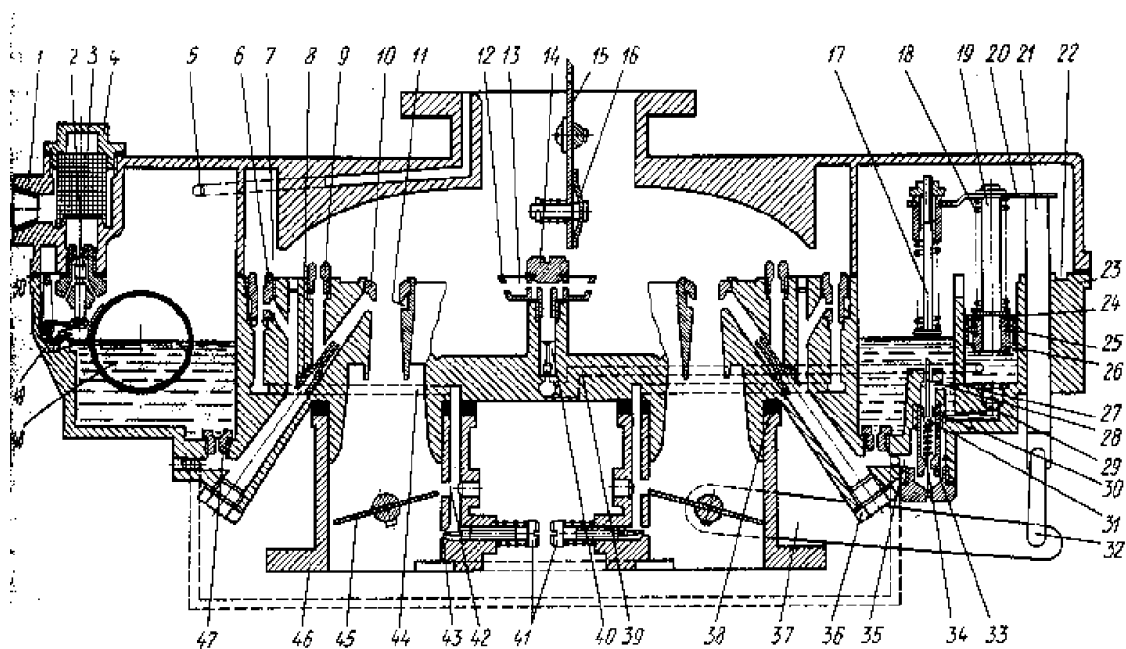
Схема карбюратора К-88АМ. 1-корпус воздушной горловины; 2-игольчатый клапан; 3-сетчатый фильтр; 4-пробка фильтра; 5-балансирующий канал; 6-корпус жиклеров системы холостого хода; 7-вырез в корпусе горловины; 8-жиклер полной мощности; 9-воздушный жиклер; 10-малый диффузор; 11-кольцевая щель; 12-распылитель ускорительного насоса; 13-воздушная полость; 14-полый винт; 15-воздушная заслонка; 16-предохранительный клапан; 17-основной толкатель; 18 и 34-пружины; 19 и 21-штоки; 20-планка (поводок); 22-кольцевая канавка; 23-корпус поплавковой камеры; 24-манжета; 25-пружина манжеты; 26-втулка штока; 27-отверстие; 28-промежуточный толкатель; 29 и 31-шариковые клапаны; 30-седло; 32-тяга; 33-клапан экономайзера; 35, 39 и 44-каналы; 36-пробка; 37-рычаг; 38 и 50-прокладки; 40-нагнетательный клапан; 41-винты регулировки системы холостого хода; 42-прямоугольное отверстие; 43-круглое отверстие системы холостого; 45-дроссельная заслонка; 46-корпус смесительных камер; 47-главный топливный жиклер; 48-поплавок; 49-пружина поплавка.
